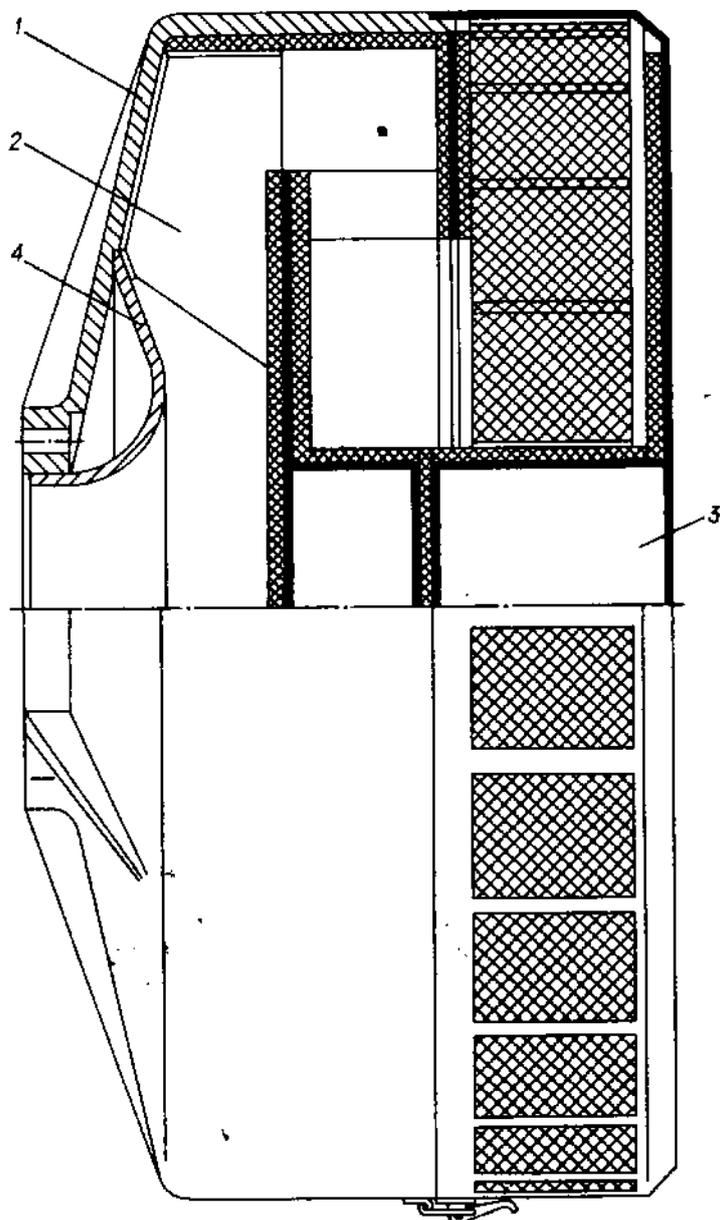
Воздухозаборник ДГРА 250/750, ДГРА 315/750: 1 - корпус; 2 - вставка; 3 - крышка; 4 - сопло
